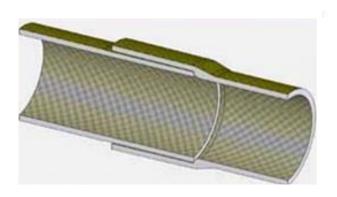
Junta en tubería FRP espiga –campana Fuente. Propia
